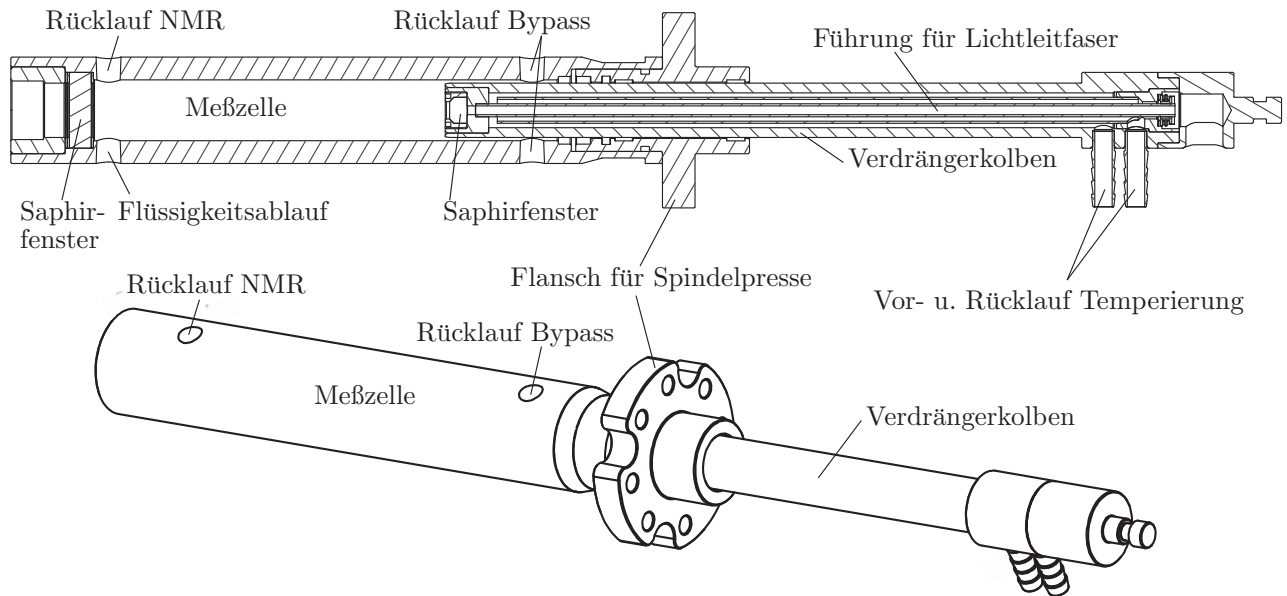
Querschnitt und Ansicht des Druckautoklavs aus Edelstahl mit Verdrängerkolben für die NMR-spektroskopische Beobachtung stark kompressibler Fluide. Innendurchmesser der zylindrischen Meßzelle 26 mm; temperierbarer, beleuchteter Verdrängerkolben (Durchmesser 25 mm, Weglänge von 203 mm, Vorschub über Handrad mit Gewindestange – nicht abgebildet), Volumen einschließlich aller Probenleitungen und Ventile 10–110 cm³, $p_{\max} = 50,0 \text{ MPa}$, $T_{\max} = 403 \text{ K}$.
